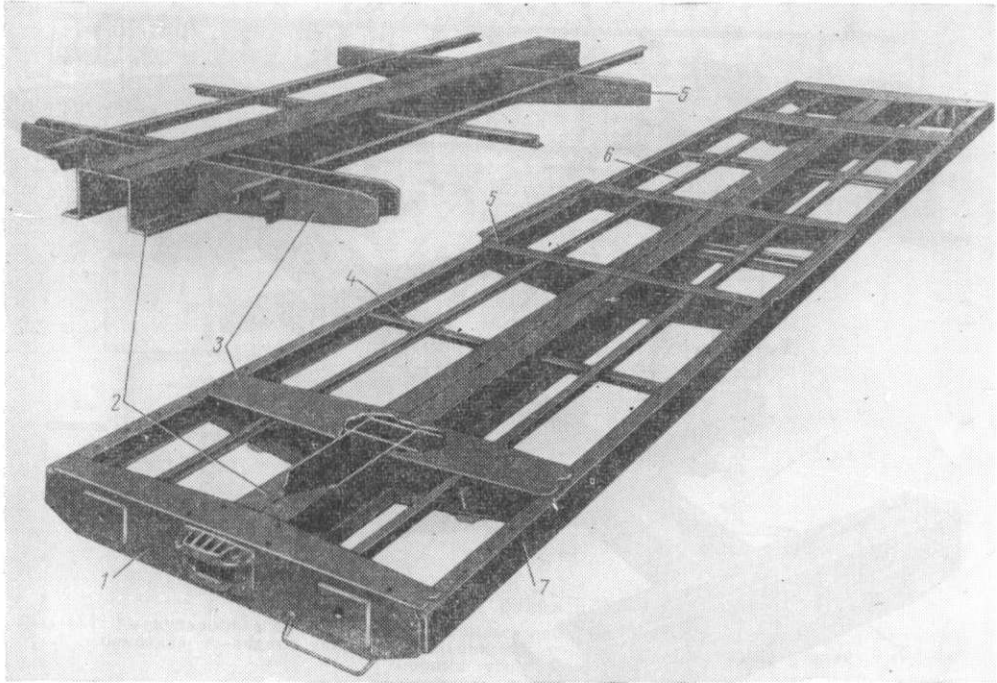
Сварная рама четырехосного крытого вагона
